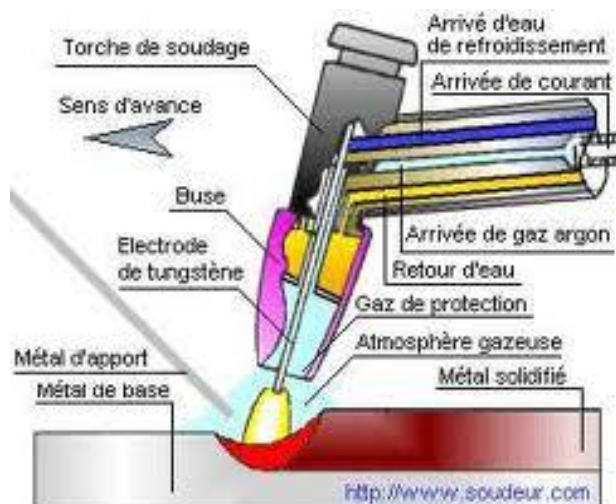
soudage TIG (Tungsten Inert Gaz) [état et mec du soudage [38]
